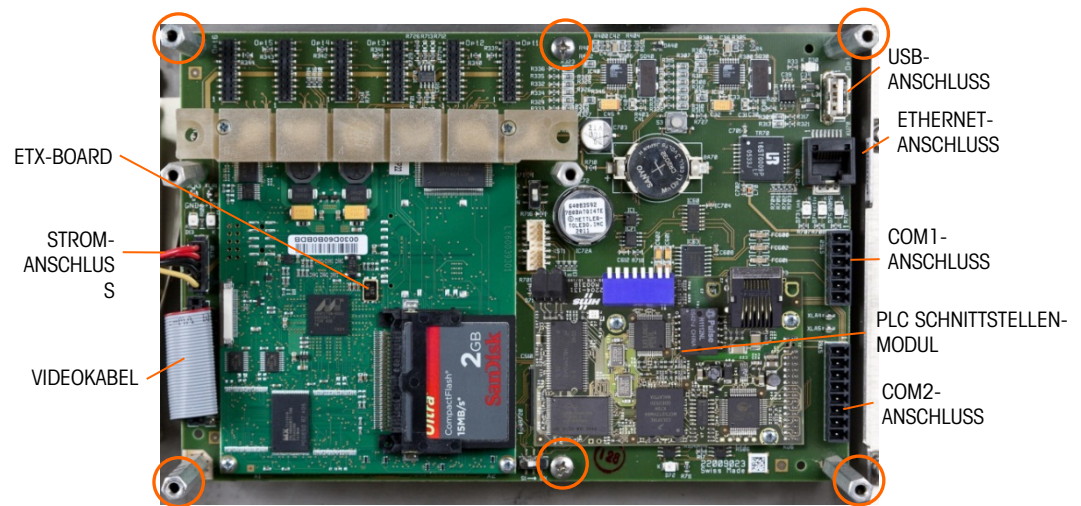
Hauptplattenanschlüsse und Befestigungsschrauben
